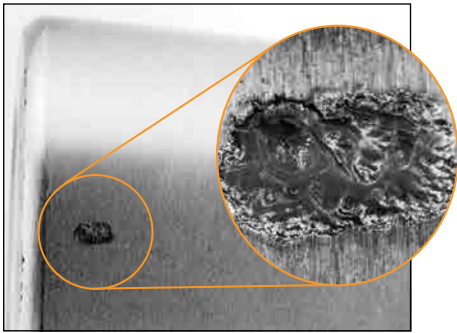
图中放大10倍后的电弧灼坑或微小灼痕，是由于轴承静止时接地不当，产生电弧造成的。
